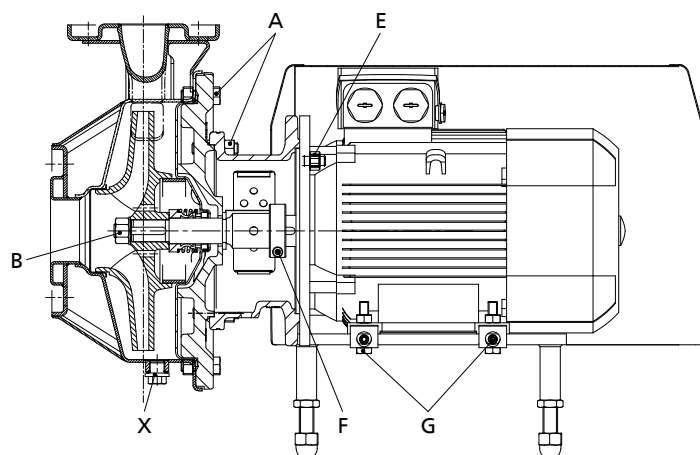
Места затяжки резьбовых соединений насоса В 050-025-250, 050-032-250, 065-040-250, 065-050-200, 065-050-250, 080-065-200, 080-065-250, 100-080-200, 100-080-250
